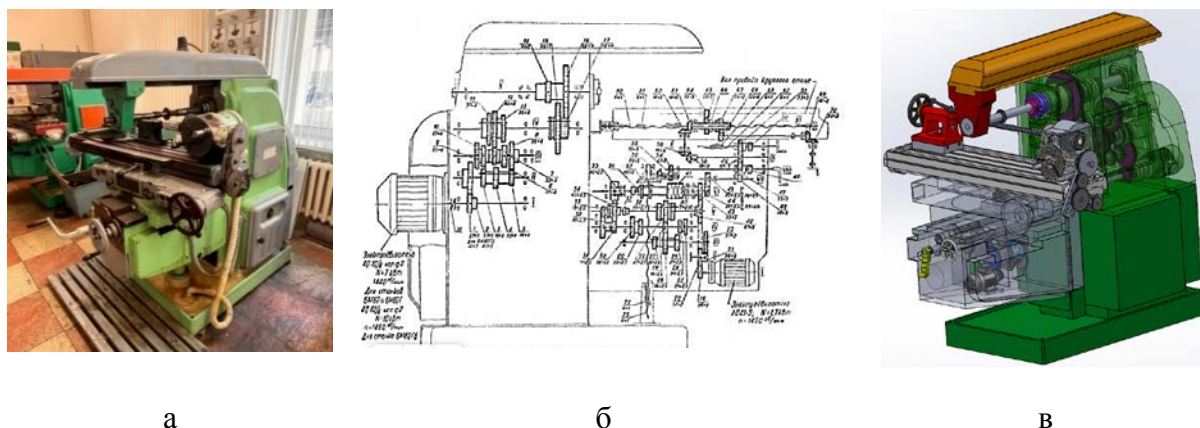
Консольно-фрезерный станок модели 6М82:
